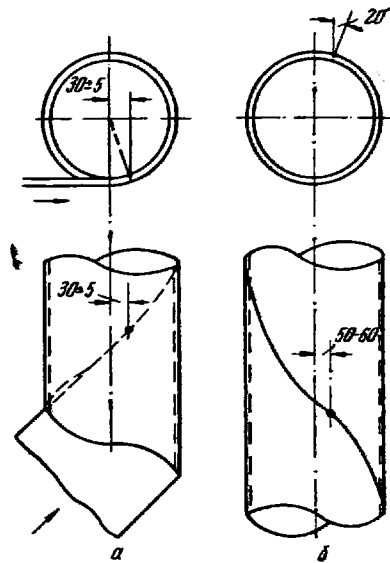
Установка электродов при сварке внутреннего (а) и наружного (б) швов
